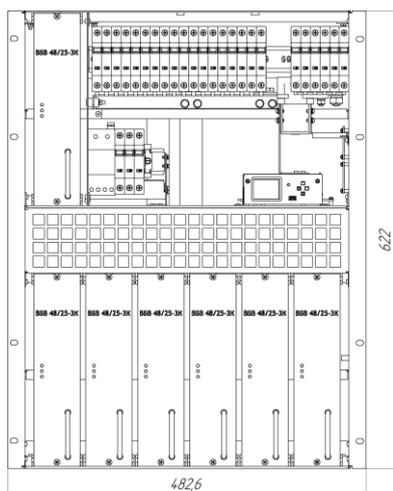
Габаритный чертеж УЭПС-ЗК 60/140, УЭПС-ЗК 48/175 (ВЭ)
